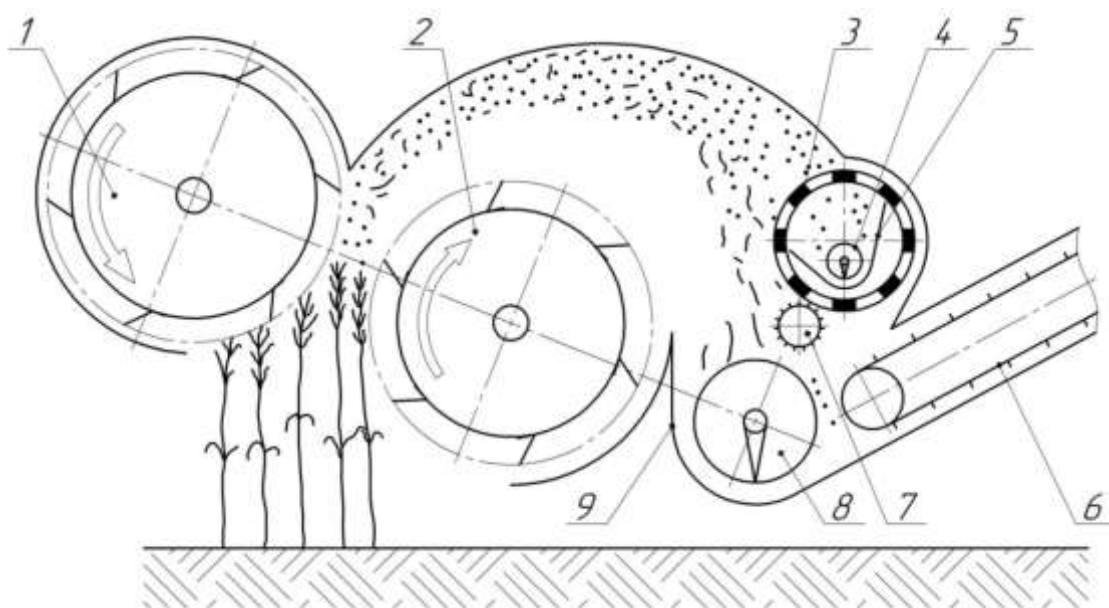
Устройство для обмолота растений на корню (SU авторское свидетельство № 1715232): 1 – подающий барабан; 2 – очесывающий барабан; 3 – цилиндрический решетчатый барабан; 4 – зерновой шнек; 5 – сборник проходовой фракции; 6 – наклонная камера; 7 – чистик; 8 – шнек; 9 – сборник
